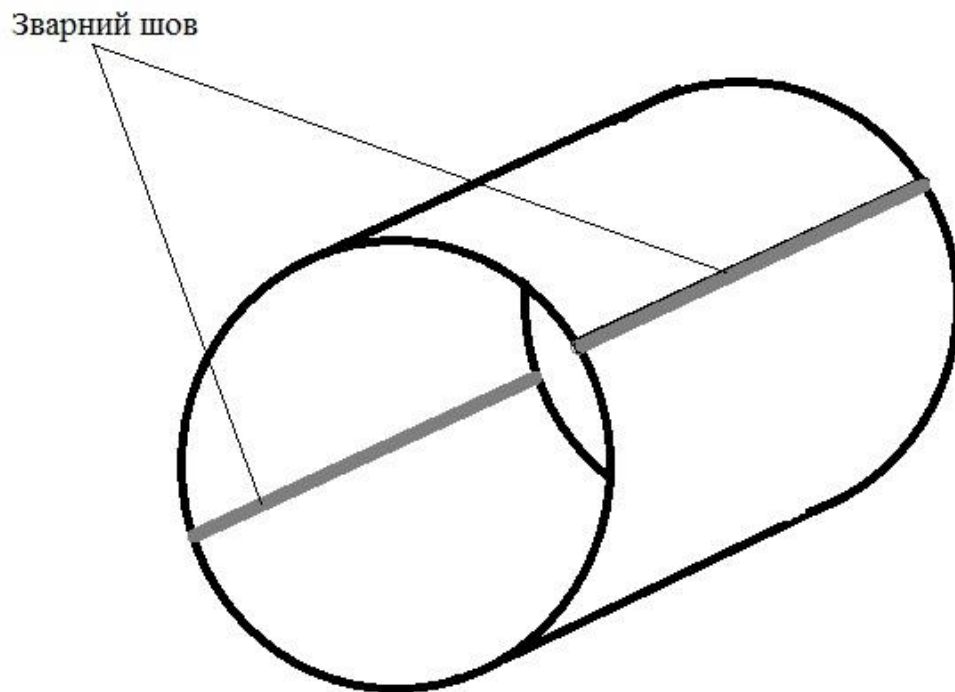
Схематичне зображення зварного стикового з'єднання
